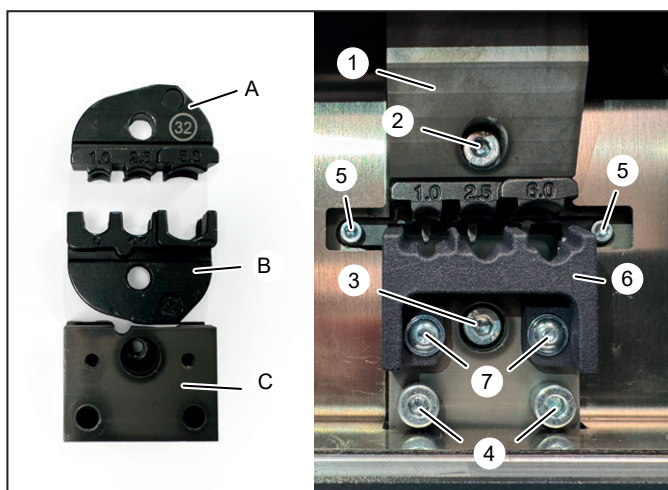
Pieza de crimpado para terminales de cable y ayuda de inserción
